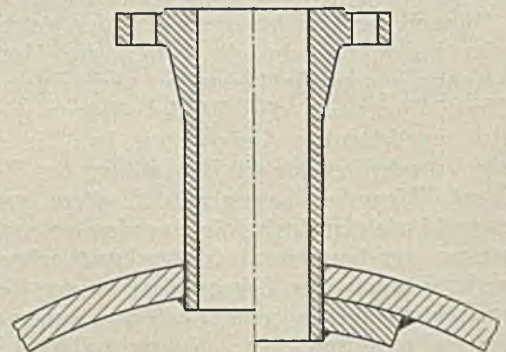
Eingeschraubter und verschweißter Stutzen.
